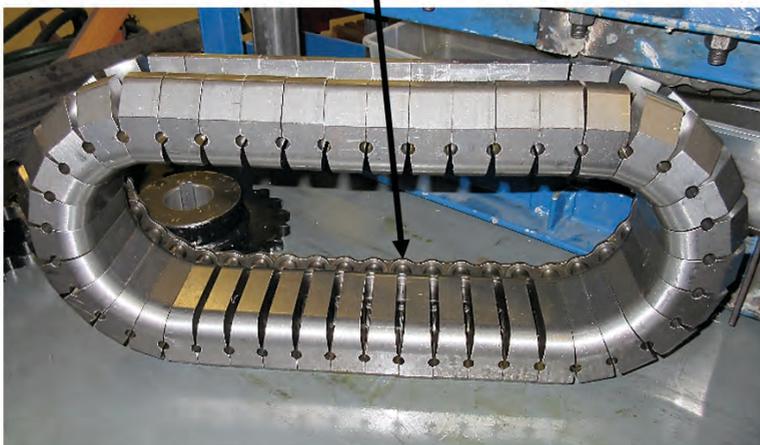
La cadena roscada, armada sobre una sola cadena de rodillos con pernos extendidos, dispuesta para recibir la segunda cadena en el primer plano de la foto
